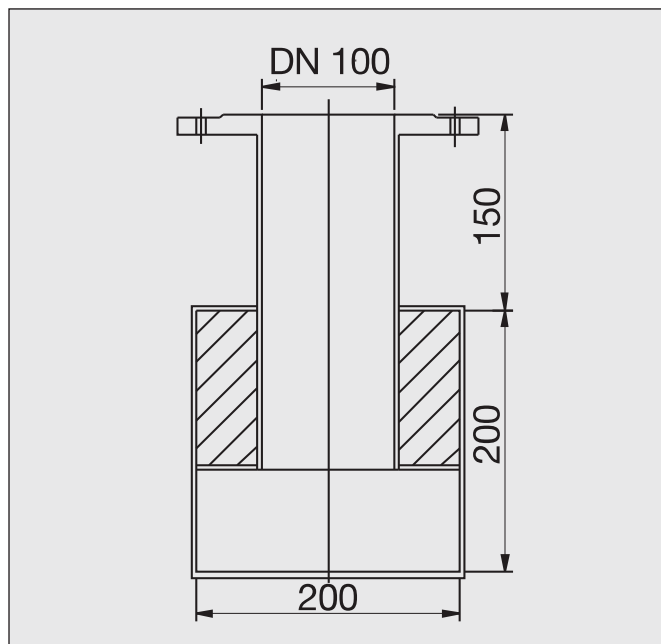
Hrdla přírub v jedné rovině, standardní délky 150mm
